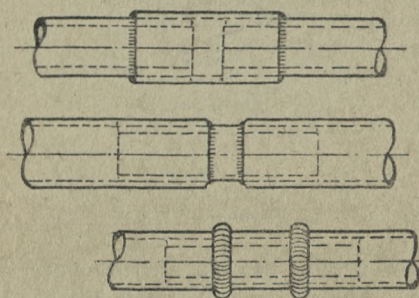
Ремонт трубчатой конструкции приваркой бужа
